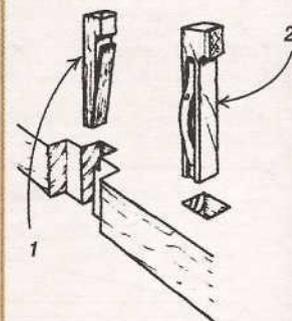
Переставляемые упоры для крепления заготовок на верхней крышке верстака:
